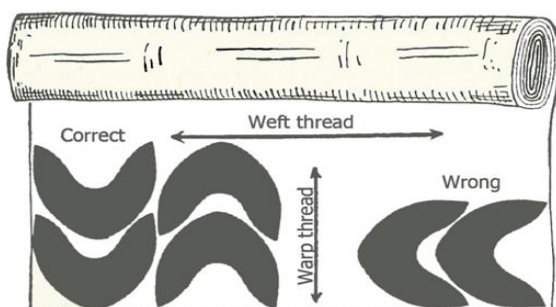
Cómo colocar las piezas del corte sobre materiales textiles
